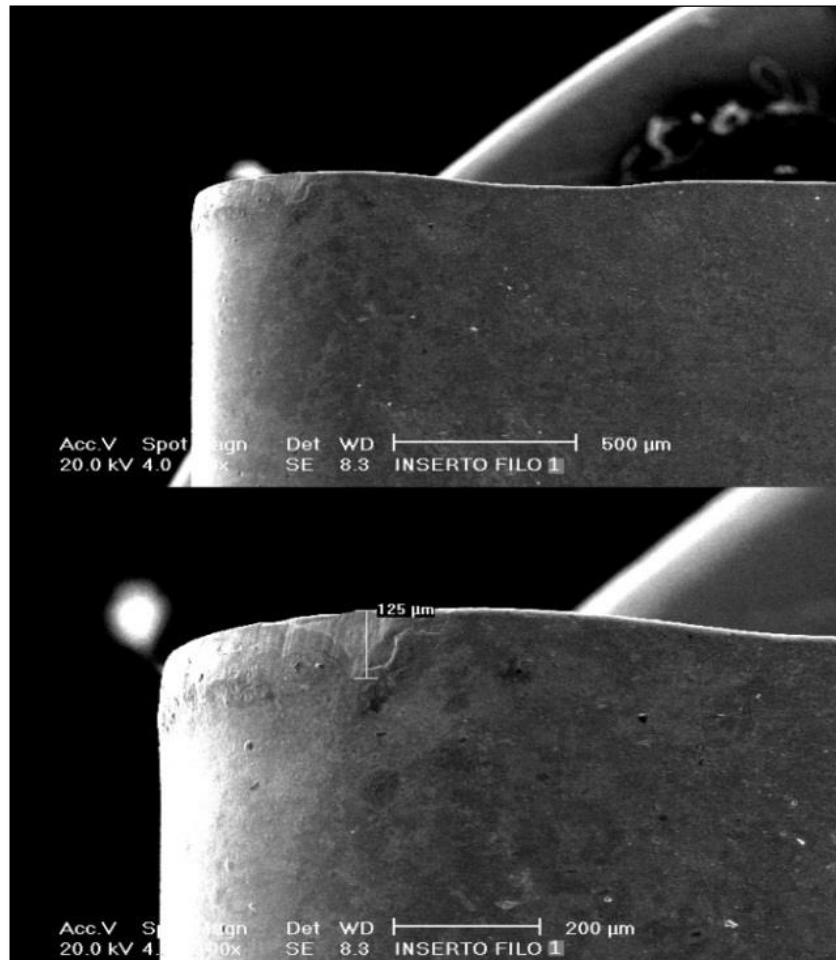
Imagen 100X Inspección del Filo de corte 1 y medición del desgaste del flanco de la herramienta.
